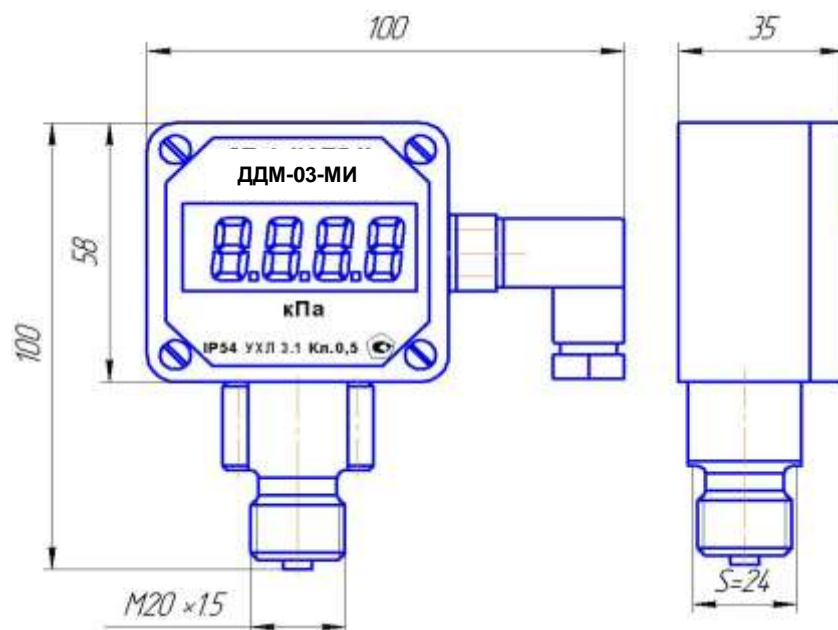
Габаритные и присоединительные размеры датчика ДДМ-03-ДИ (ДВ, ДИВ, ДА)-МИ-03
